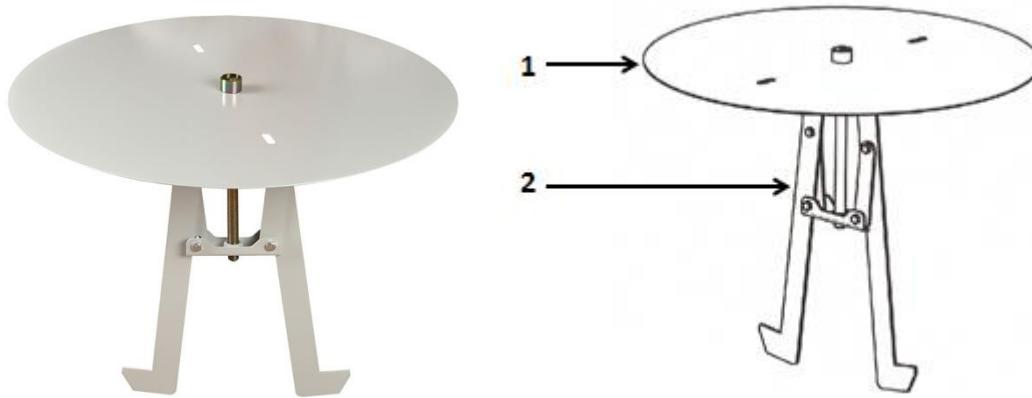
Устройство УЗНКЛО-1 ССД: а – внешний вид в сборе;
